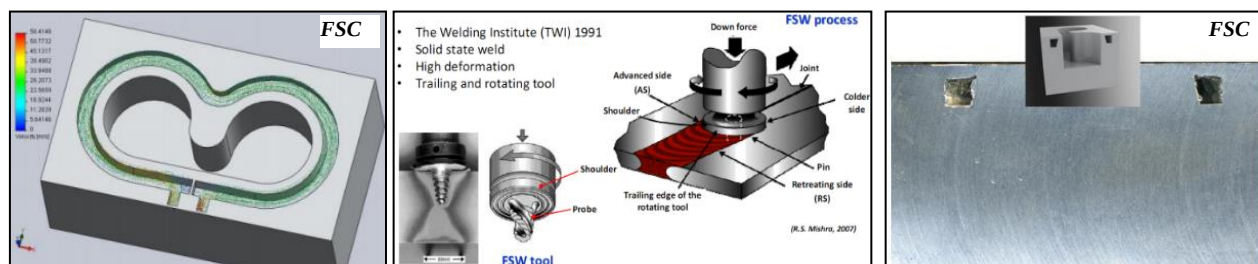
Acima: princípio da soldagem Friction Stir Welding; Abaixo: confecção de canais por Friction Stir Channelling [4]
